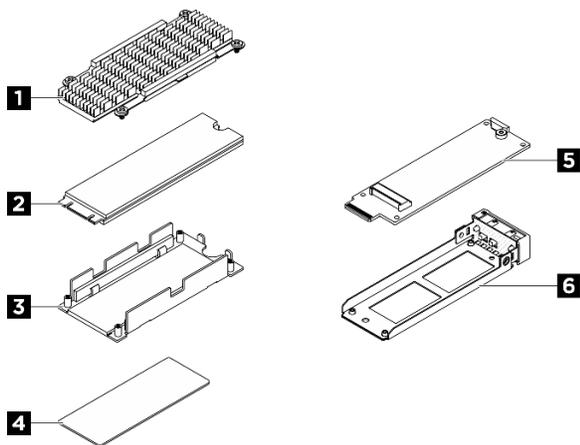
Partes de um conjunto de unidade M.2 hot-swap
